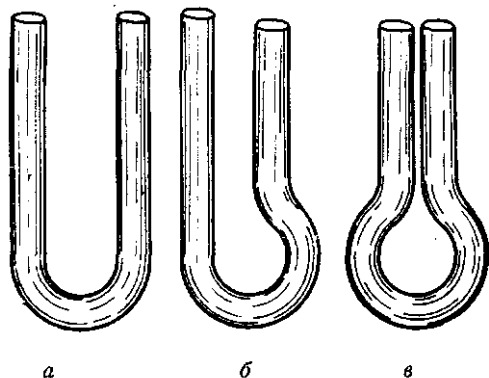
Кольцевой изгиб трубки: а — U-образный изгиб; б — изгиб одного колена; в — изгиб двух колен — готовое изделие-
